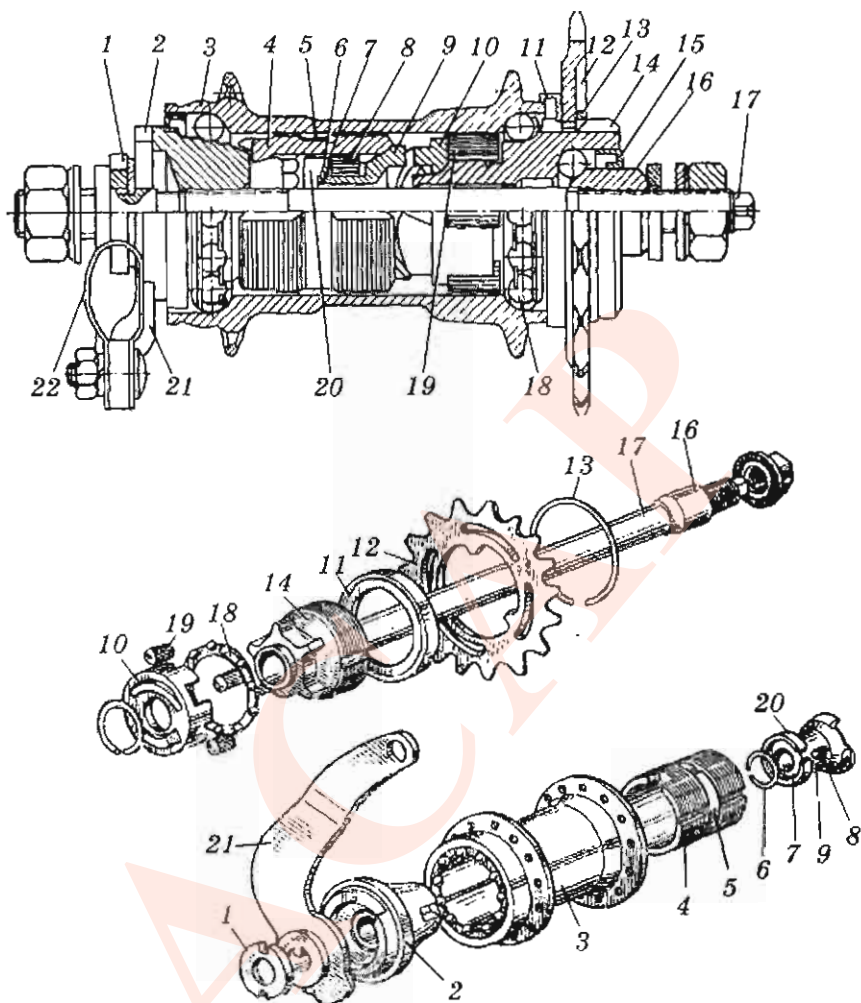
Конструкция (а) и детали (б) втулки заднего колеса типа «Торпедо»:
